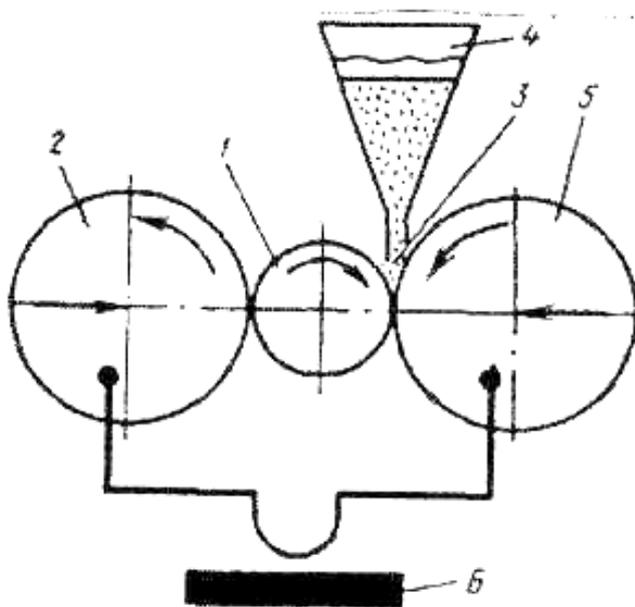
Схема восстановления и упрочнения деталей типа «вал» порошковыми материалами:
